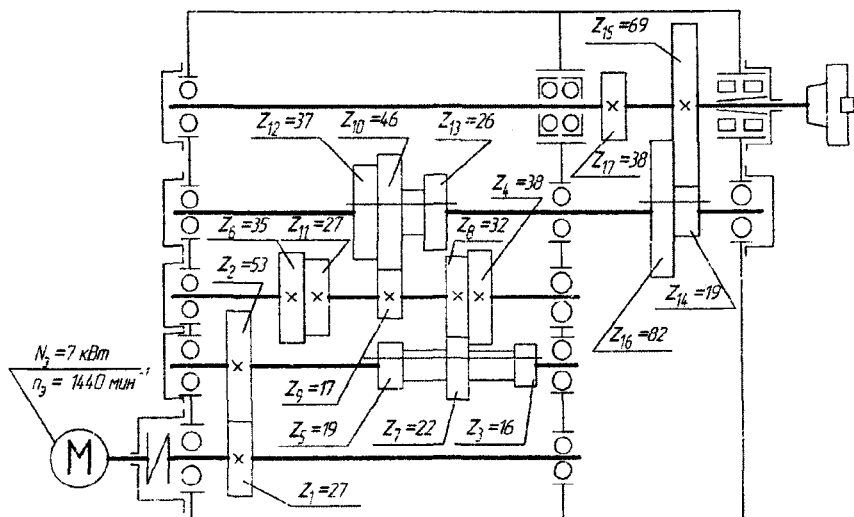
Кинематическая схема главного привода горизонтального консольно-фрезерного станка модели 6М82
